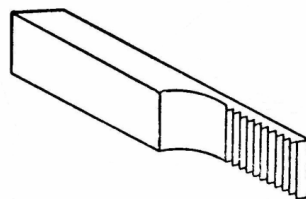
Гребенка для изготовления рифлений в пазах фрез
